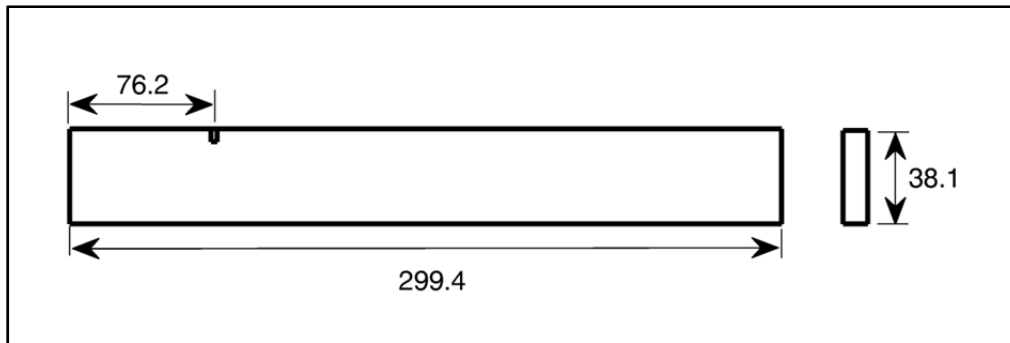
Dessin schématique du spécimen sous forme de poutre (dimensions en mm)
